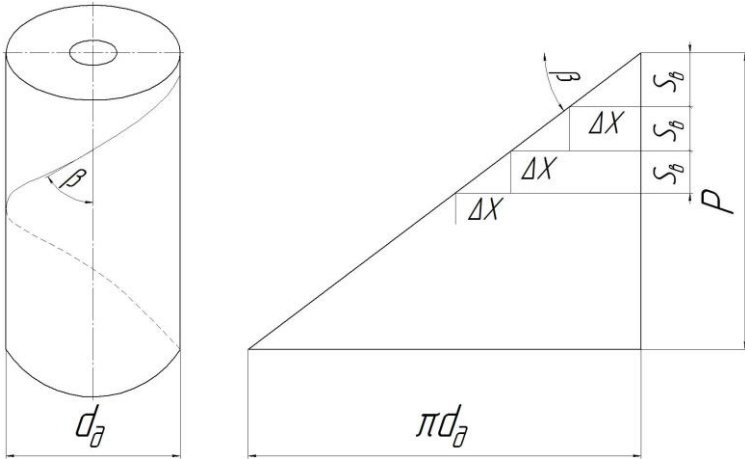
Перемещение фрезы относительно заготовки при нарезании косозубого колеса
